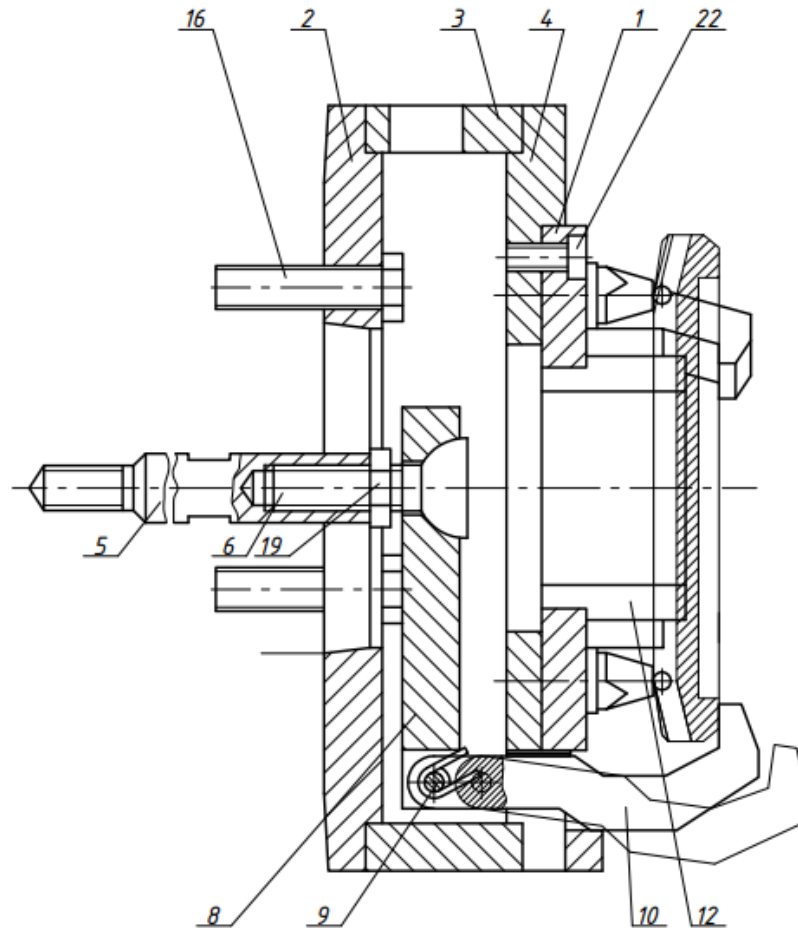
Пристрій для шліфування $\varnothing 175H7$ і торця в деталі КС6В-47.638
